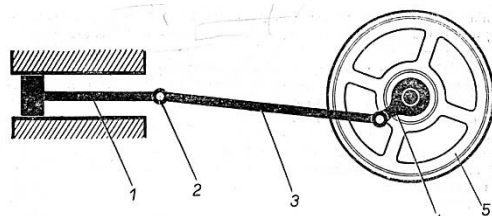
Кривошипно-шатунный механизм двигателя Д.Уатта
